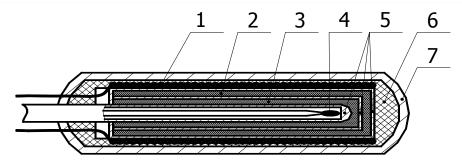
Самокалибрующийся датчик температуры (1 – управляемый нагревательный элемент; 2 и 3 – реперные металлы; 4 - первичный измерительный преобразователь (ПИП); 5 – тигли, выполненные из никеля; 6 - порошок окиси магния; 7 – металлический корпус)
